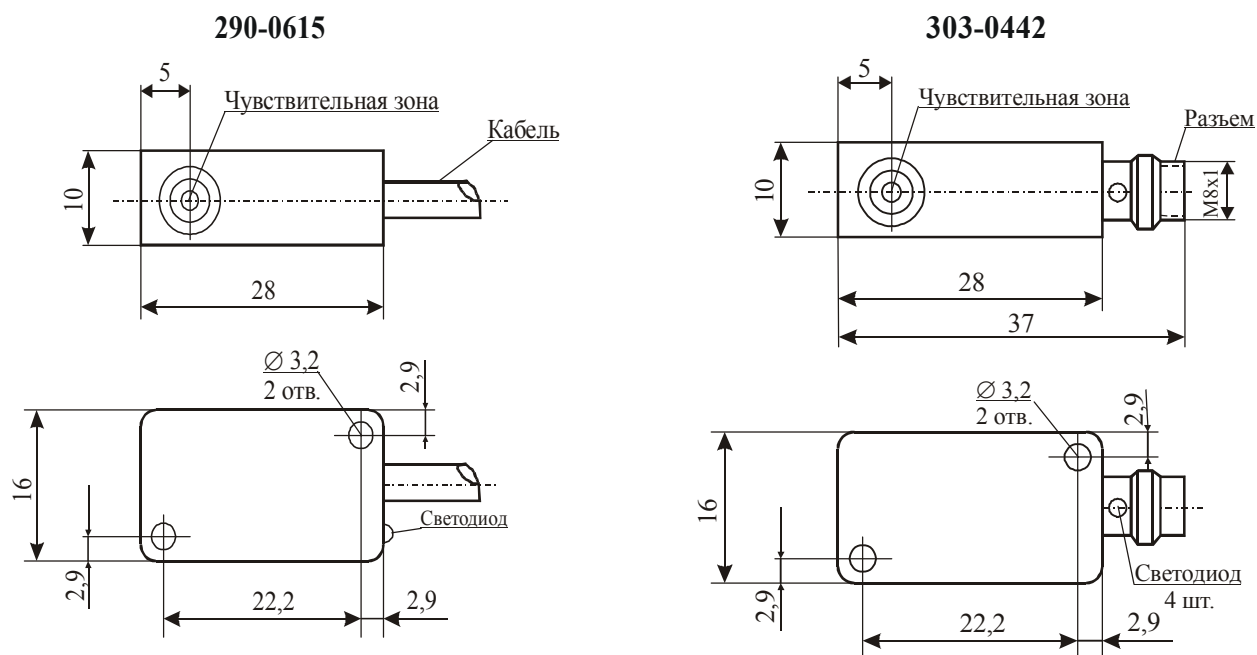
Внешний вид и габаритные размеры датчиков типа 29-0615 и 303-0442
